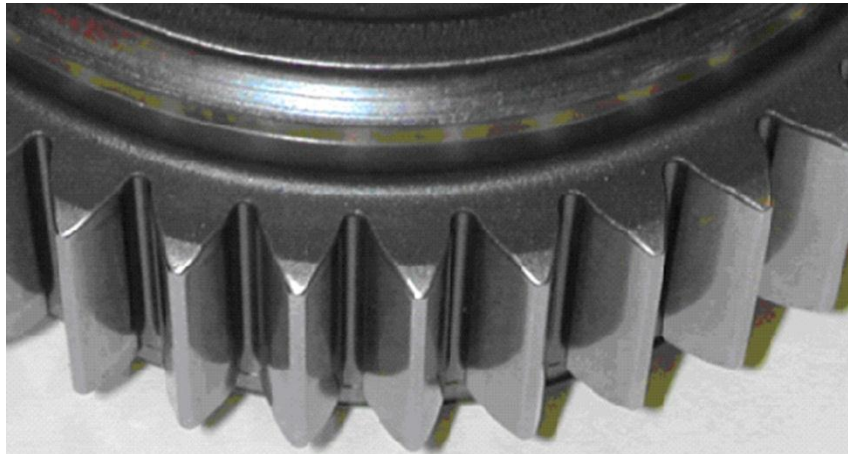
Зубці колеса з несиметричними профілями: основний профіль 33° , прямий 25°
